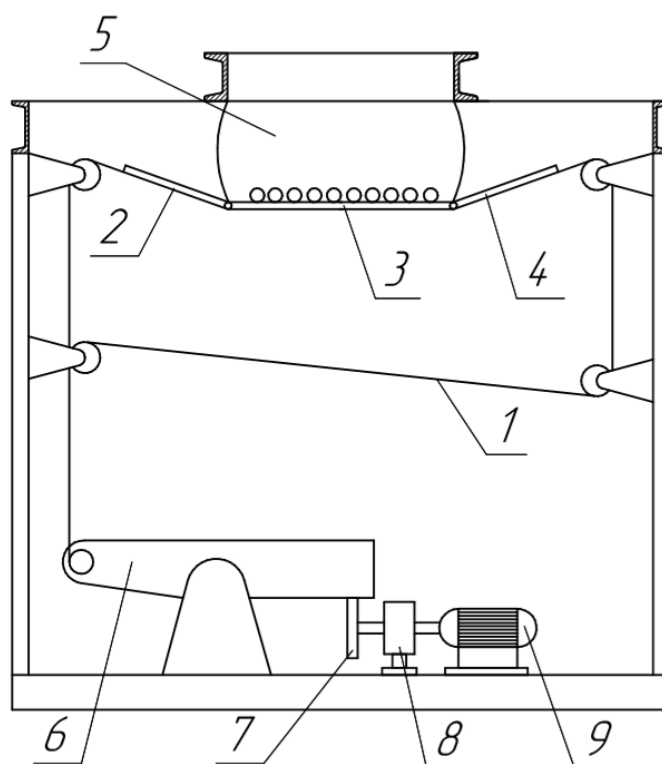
Принципиальная схема устройства для вибрационной ударно-импульсной обработки деталей: 1 – гибкая нить; 2, 3, 4 – жесткие площадки; 5 – рабочая камера; 6 – кулиса; 7 – кулачок; 8 – редуктор; 9 – двигатель
